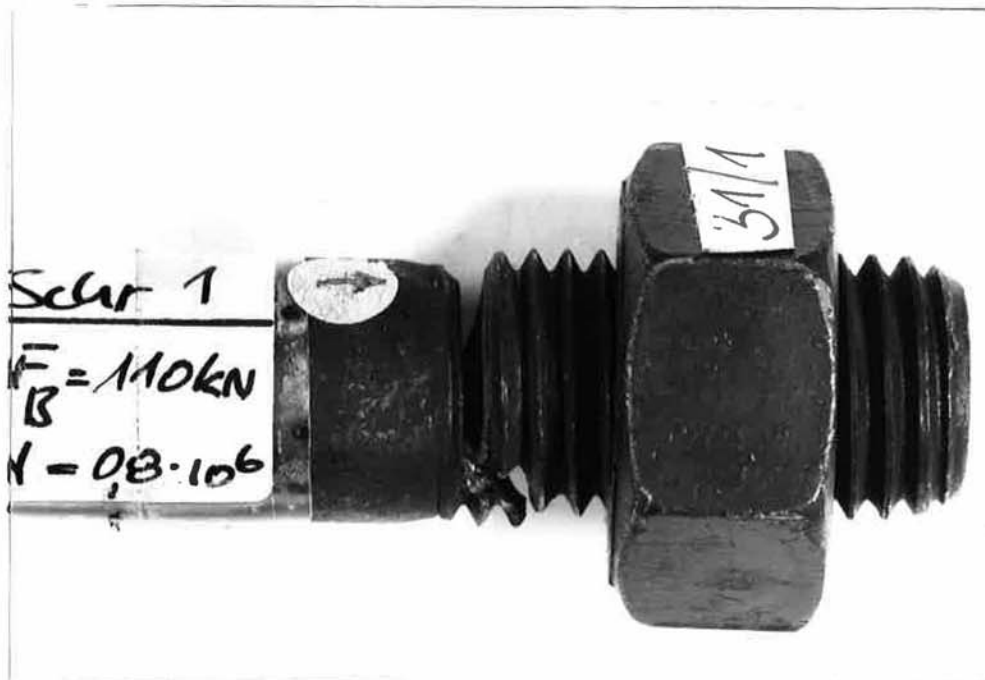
Dauerschwingbruch im ersten belasteten schaftseitigen Gewindegang einer hochfesten Schraube M 20. Schraube a des Versuches Nr. 31 (Versuchsreihe 1). Anrißstelle (Pfeil) zugblechseitig
